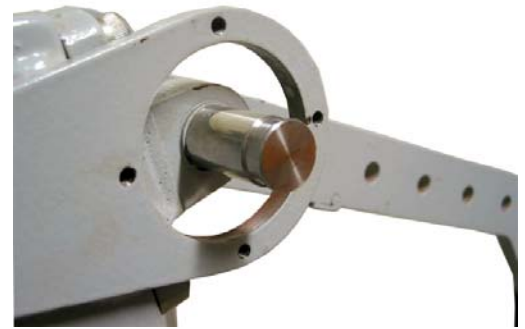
Base do ACP Rotativo montada com o Cilindro
